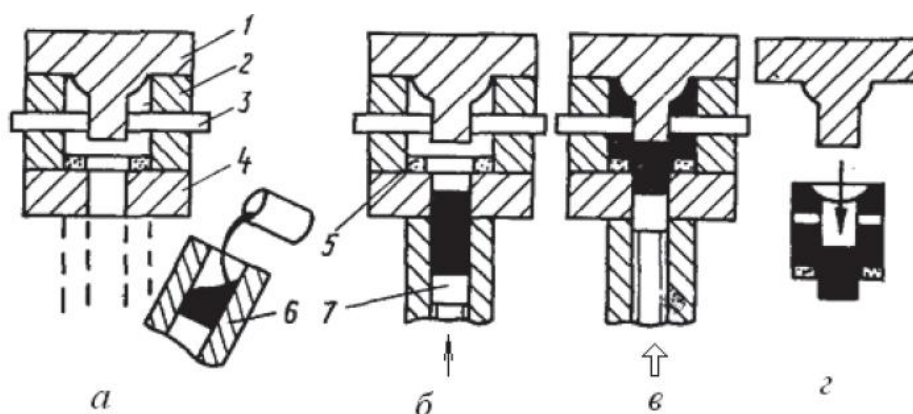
Изготовление поршней способом ЛКД на литейной машине с нижним узлом прессования: *а* – заливка металлического расплава в металлоприемник; *б* – начало вытеснения расплава из металлоприемника в матрицу; *в* – уплотнение затвердевающей отливки; *г* – съем отливки с верхней полуформы; 1, 2, 4 – детали пресс-формы; 3 – стержень; 5 – керамическая вставка; 6 – металлоприемник; 7 – пуансон (плунжер).
